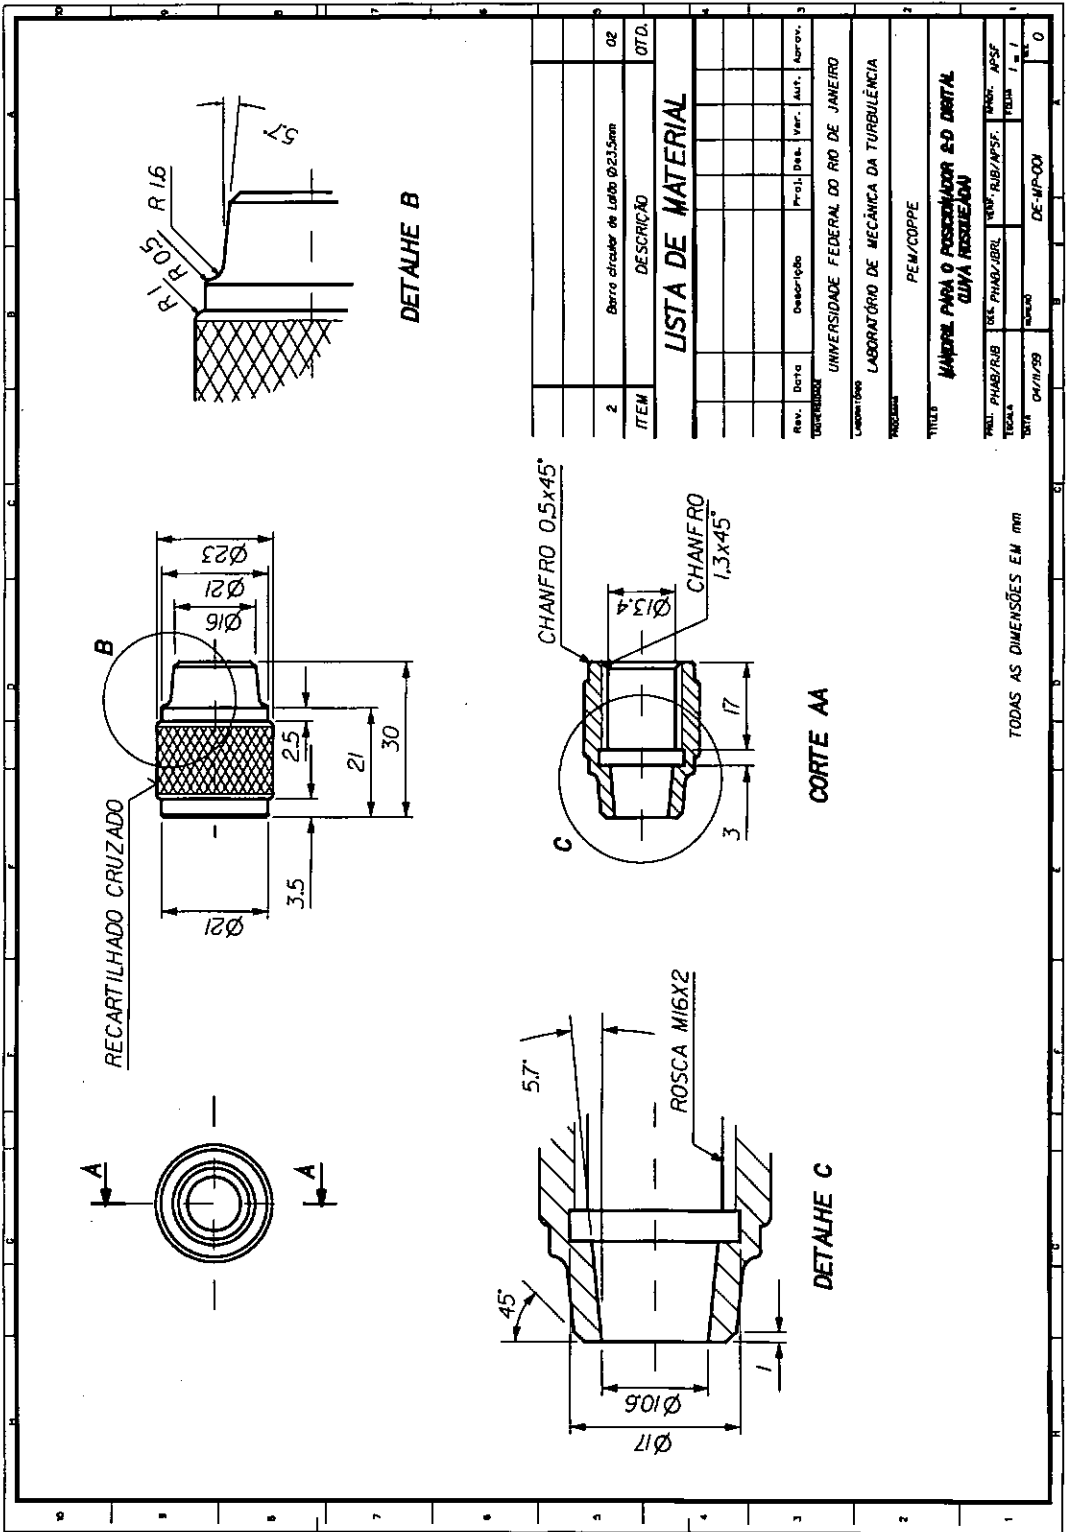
Parte do desenho técnico do conjunto bucha-mandril projetado para o posicionador 2D utilizado nos experimentos (peça: luva rosqueada).
